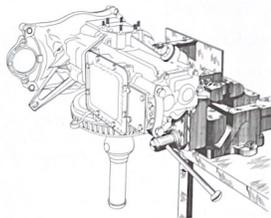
Posición de la caja para el reglaje del juego en los rodamientos del diferencial.
